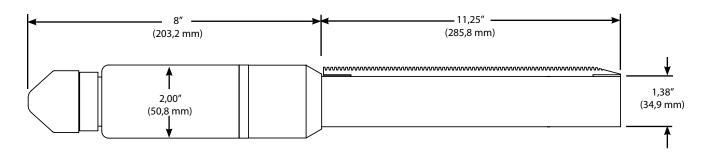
Dimensiones del soplete PT-26 "SL" In-line
